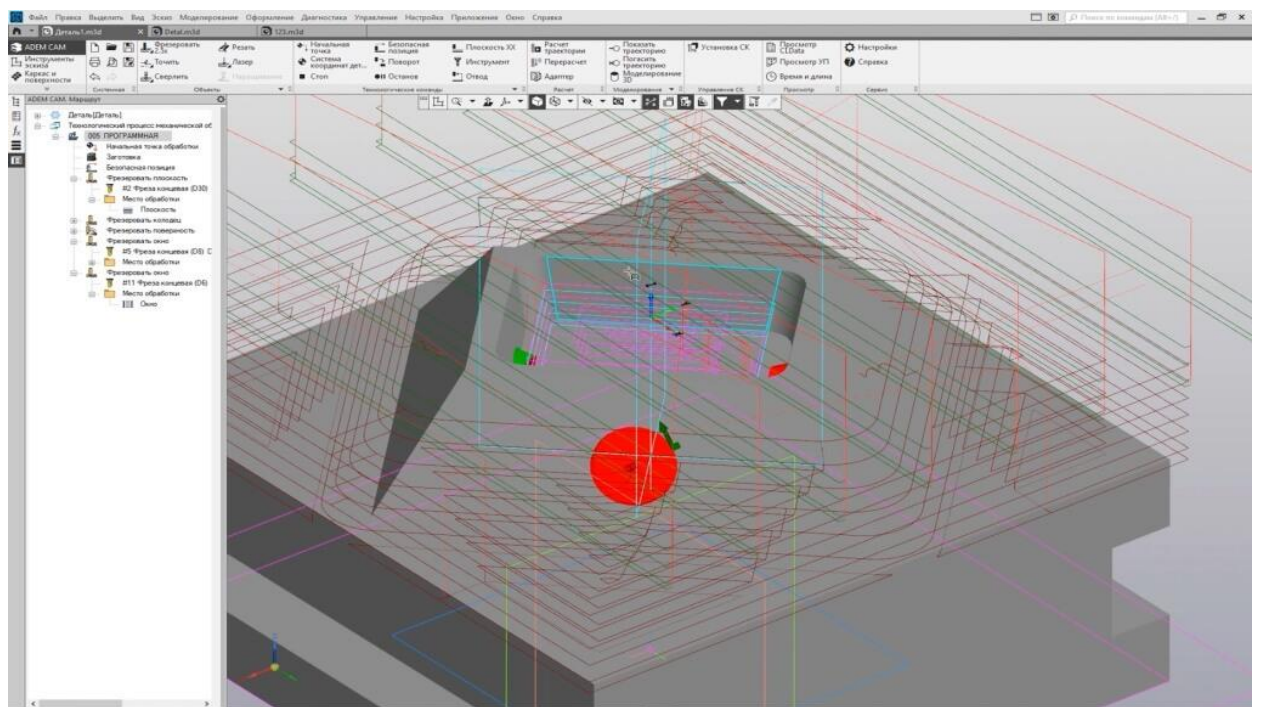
Модуль ЧПУ. Фрезеровка
